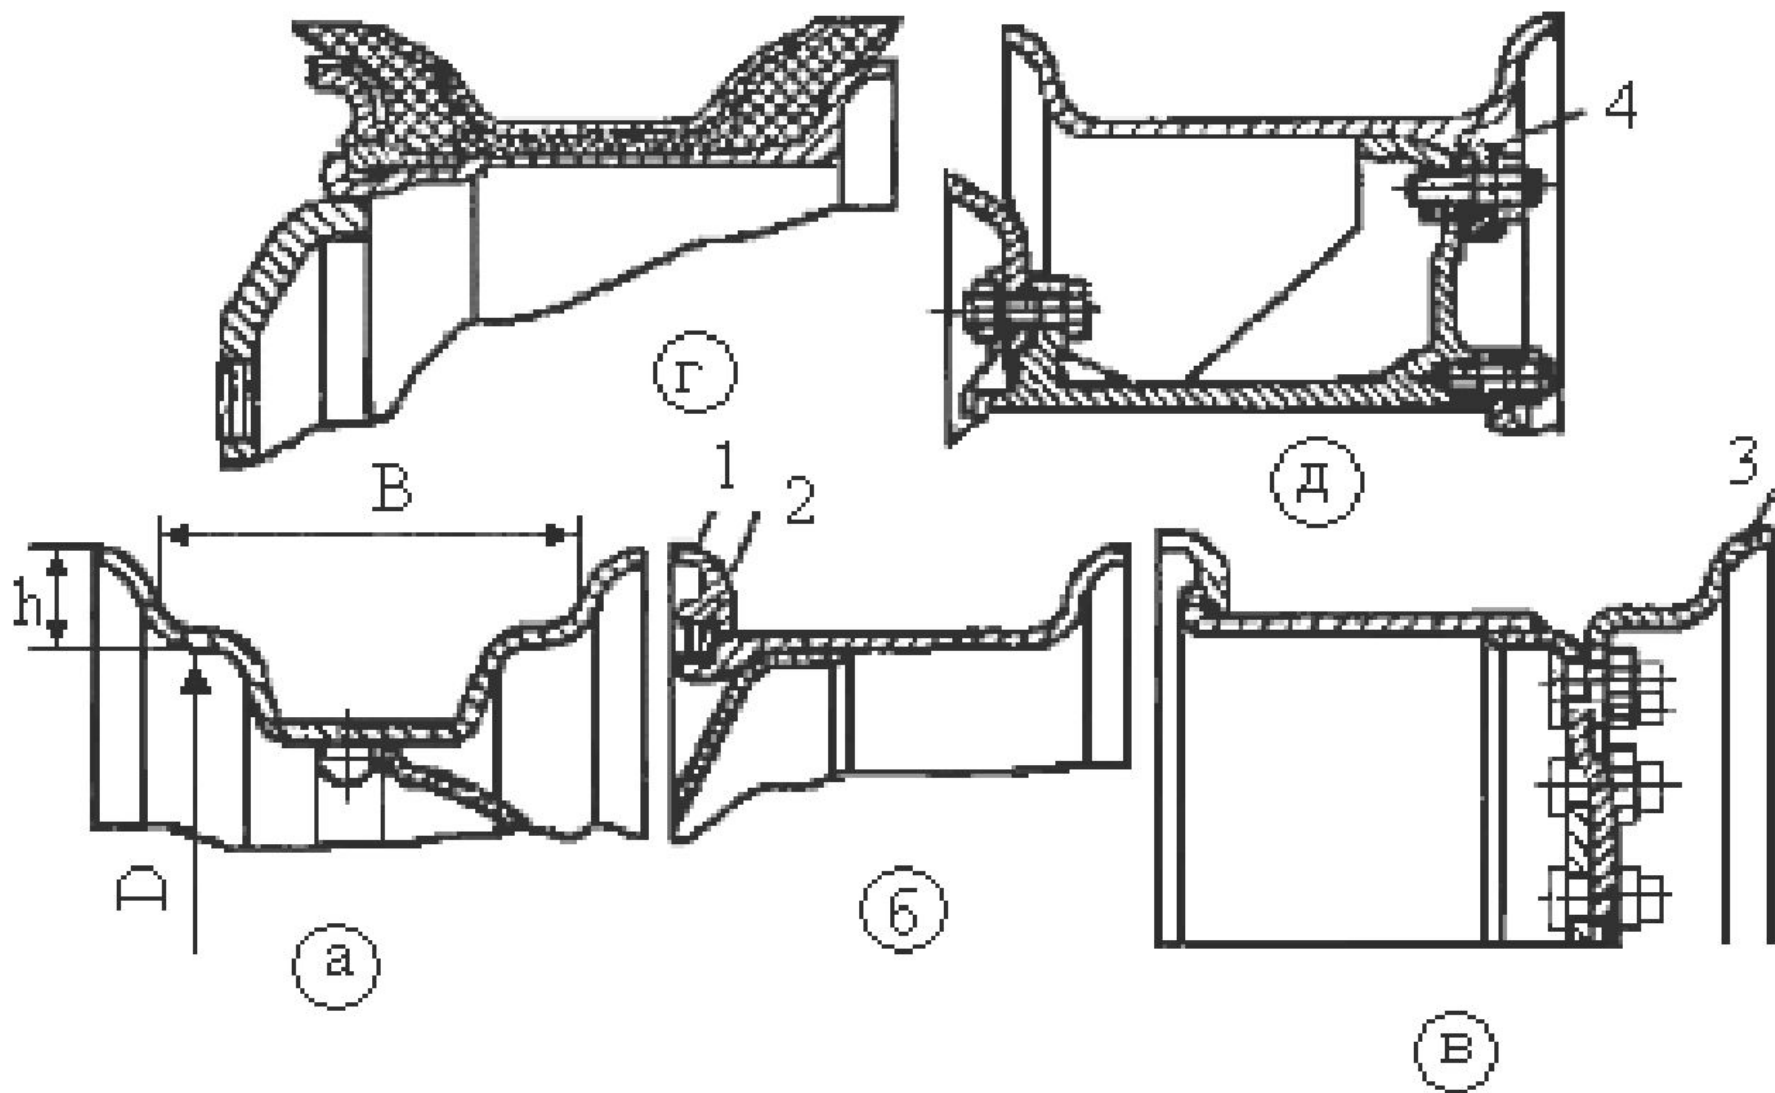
Типи ободів коліс: а-глибокий нерозбірний симетричний; б-плоский розбірний з бортовим і замковим кільцями; в-окремим бортом; г-розширений з конічними полками; д - бездискове колесо
